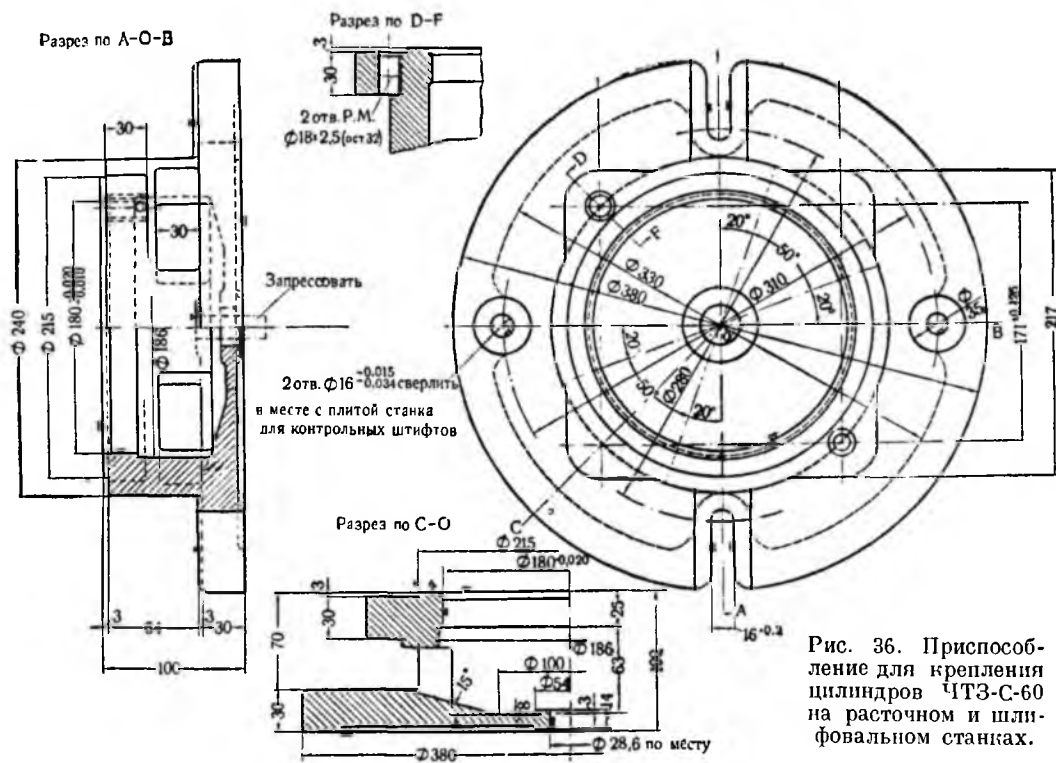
Приспособление для крепления цилиндров ЧТЗ-С-60 на расточном и шлифовальном станках.
